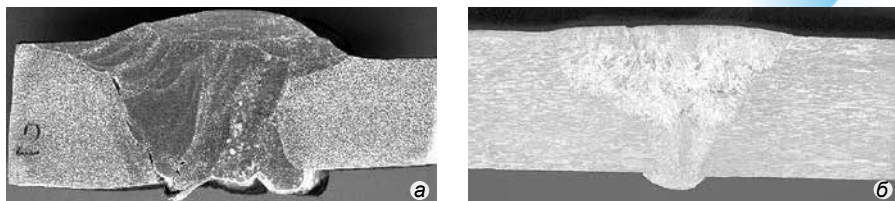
Ремонтные швы на кислородном регенераторе из сплава АМг6, выполненные ручной аргонодуговой сваркой неплавящимся электродом (толщина соединяемых деталей 16 мм + 12 мм) (а) и ручной плазменной сваркой (20 мм) (б).
